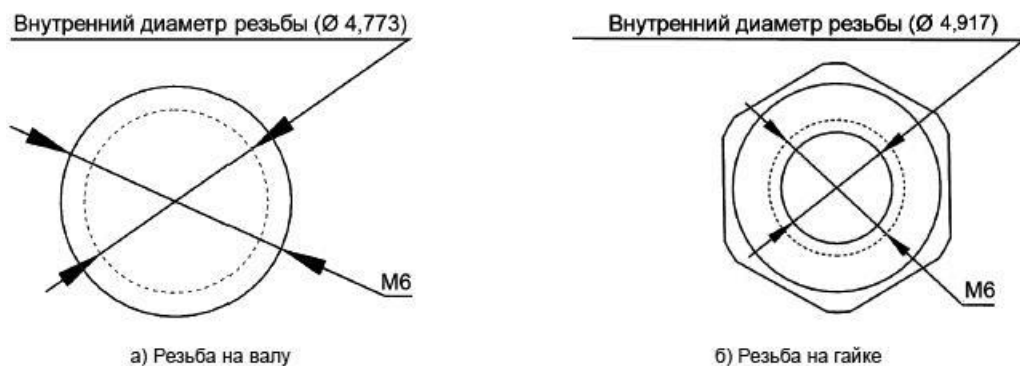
Примеры ЭМД с резьбой М6 согласно [ГОСТ 24705](https://www.gost.ru/standarts/gost/24705)
